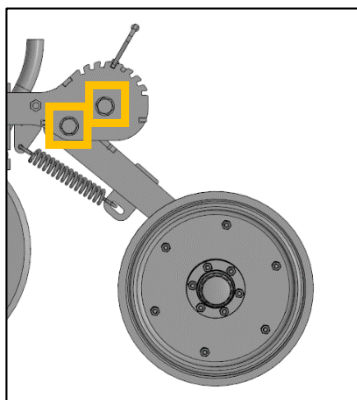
Втулки оси качения укрывающих колёс и ось рычага фиксатора
